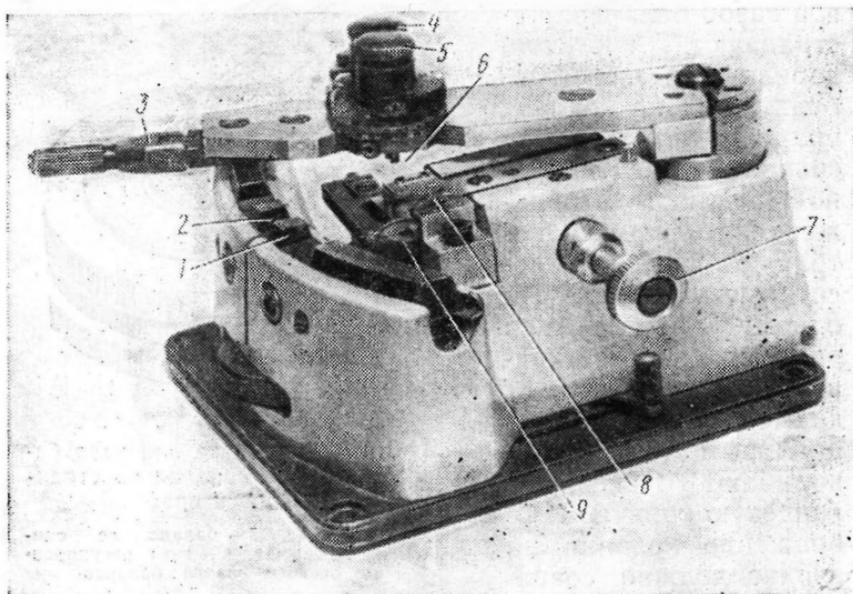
Приспособление для гибки концевой кривой плоской спирали:
